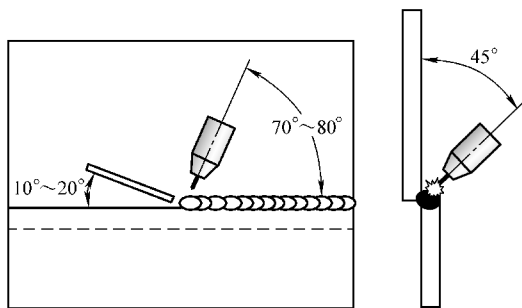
搭接横焊时焊枪焊丝正确位置
